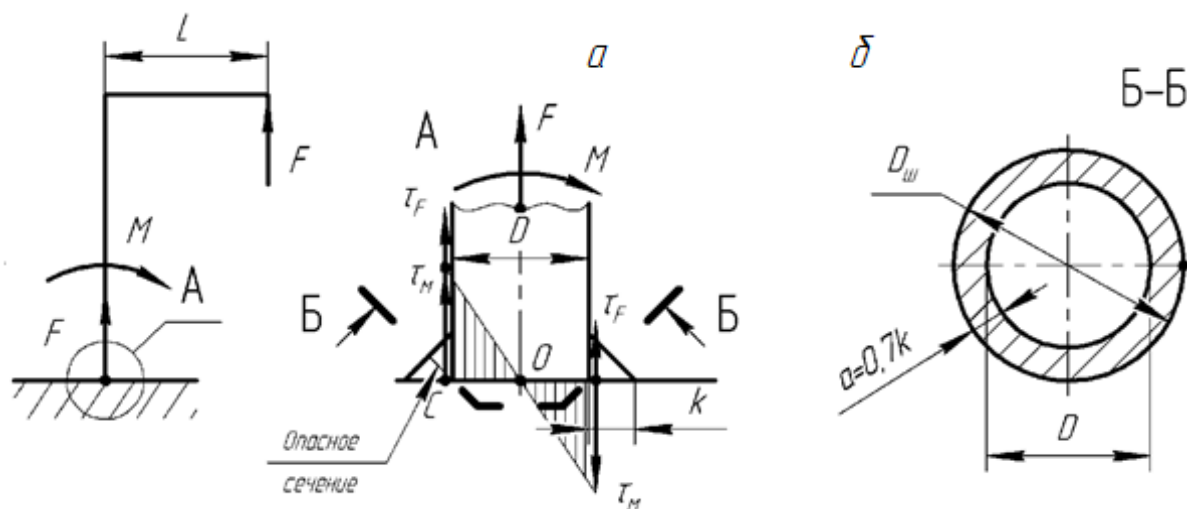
Расчетная схема сварного соединения (шва):
